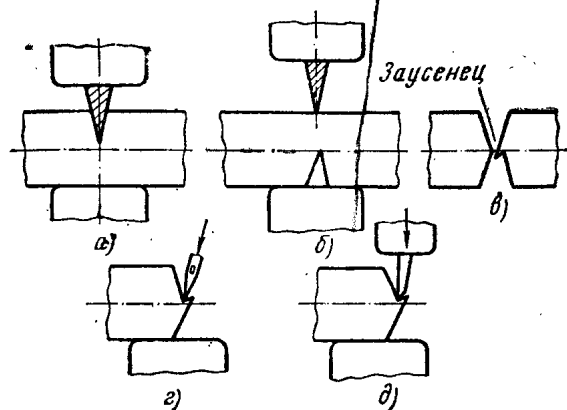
Схема разрубки под молотом с двух сторон без перемычки:
